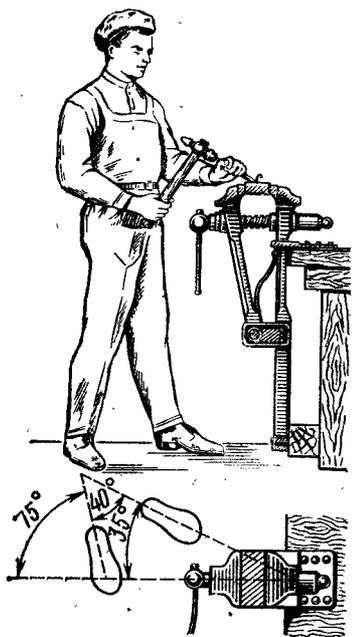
Положение ступней ног и корпуса работающего при рубке
